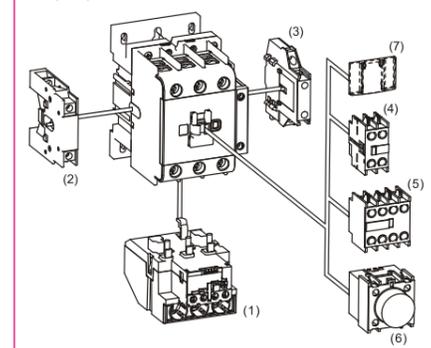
Контактор KM-102 и схематическая установка аксессуаров
